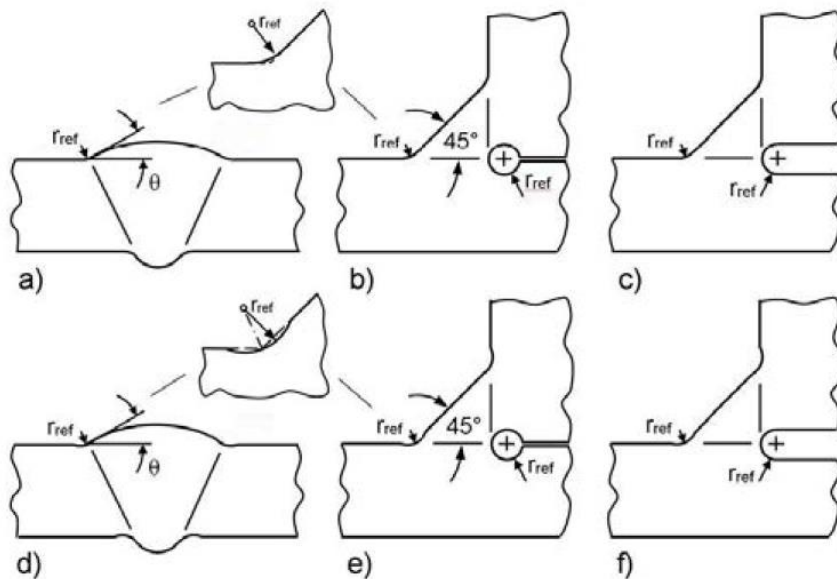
Idealisierung von Schweißnähten [2]
